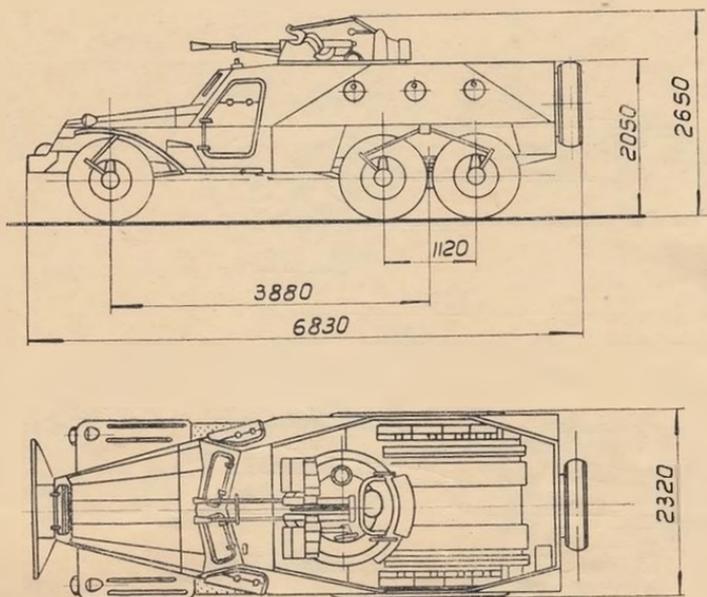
Общий вид и габаритные размеры бронетранспортера БТР-152Е.
